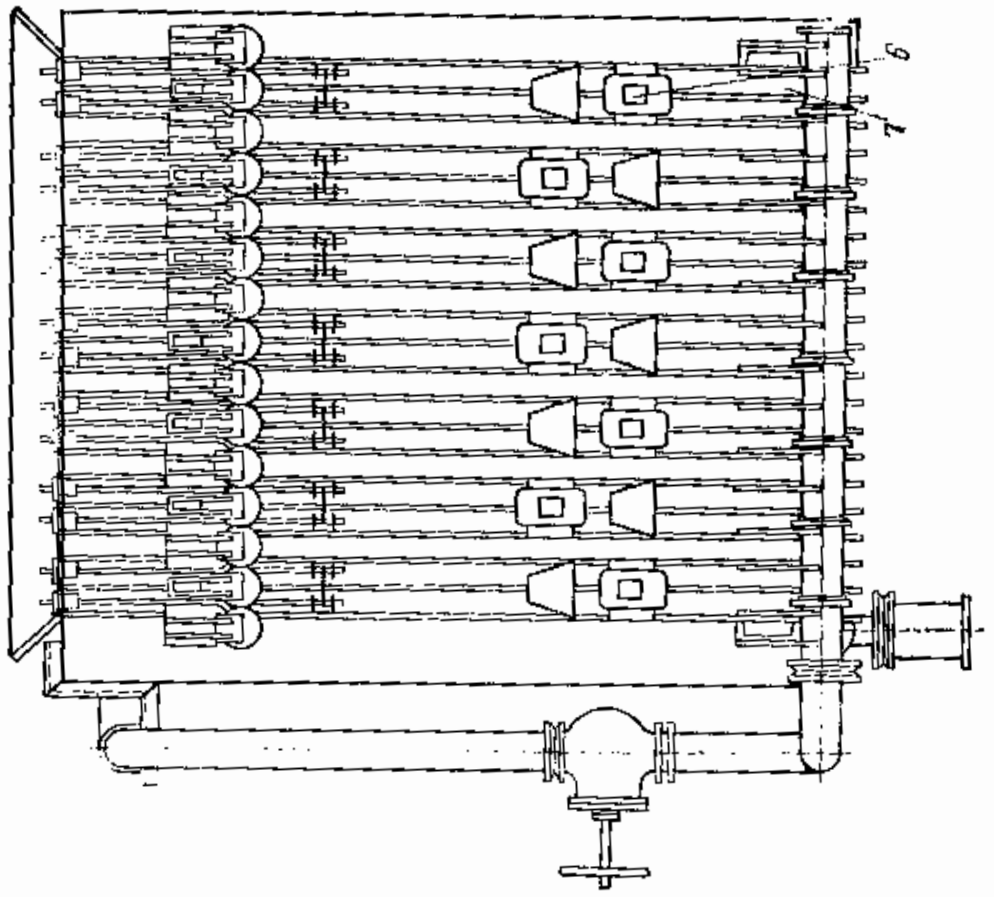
Кассета СМЖ-253 для вертикального формования железобетонных изделий:
